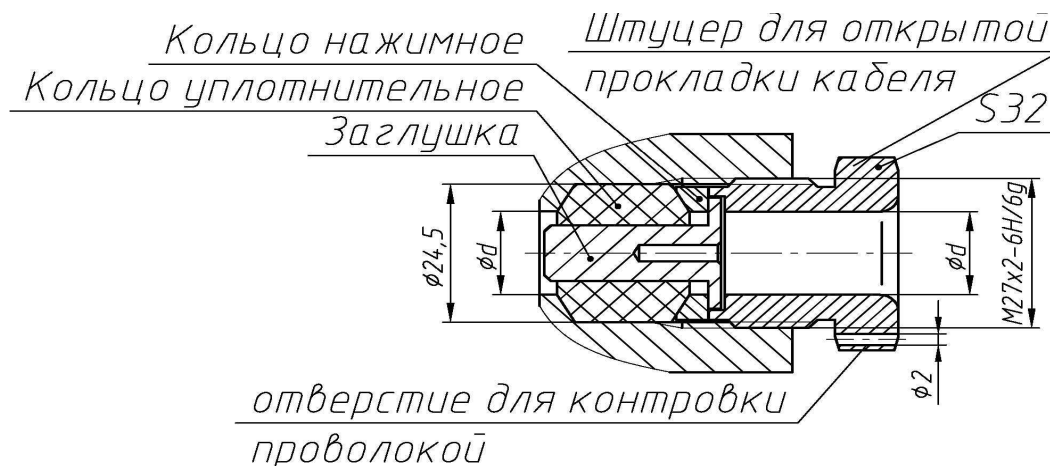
Элементы взрывозащиты кабельного ввода для открытой прокладки кабеля
